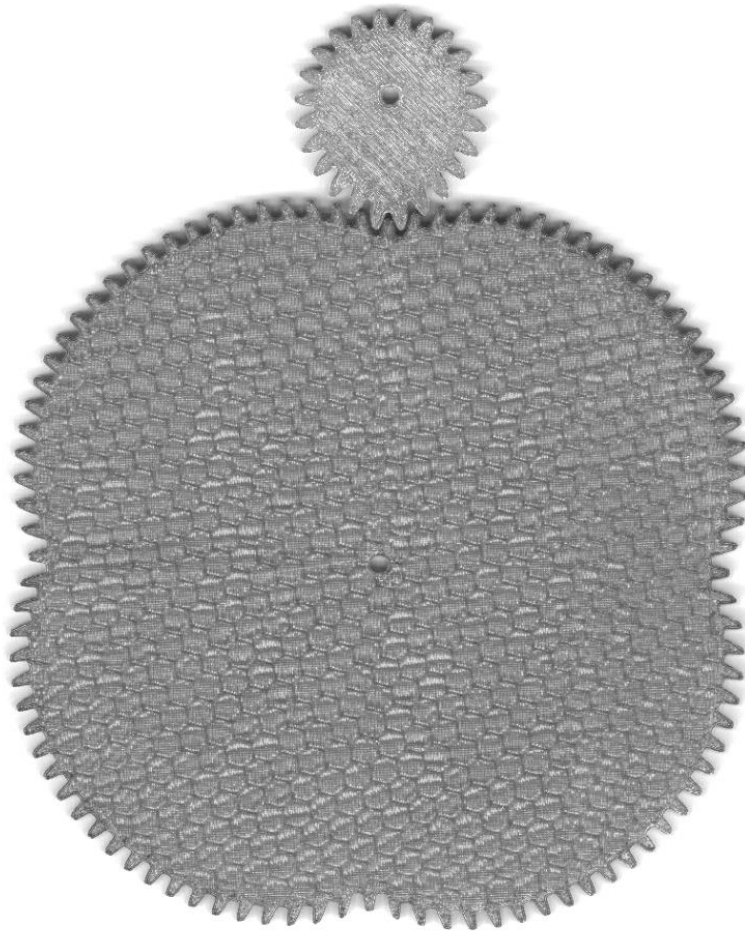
Изготовленные пластиковые прототипы некруглых зубчатых колес
